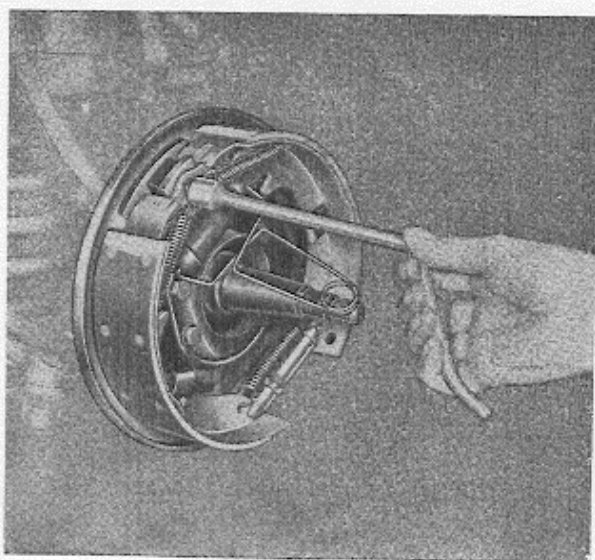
Ausbau der Rückholfeder mit einem Bremsfederwerkzeug (Snap-on BT 11 oder entsprechendes).
